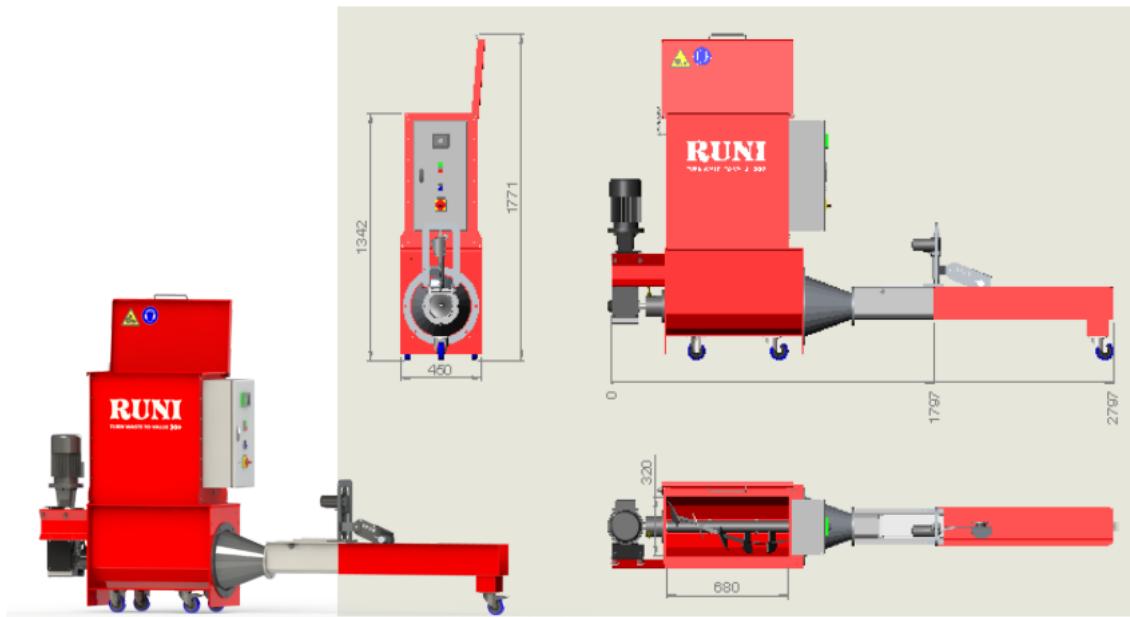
Dibujo dimensional de la compactadora SK 120 A RUNI. Fuente: RUNI Danish engineering <https://www.compactadora-runi.es/compactadores/sk120>
